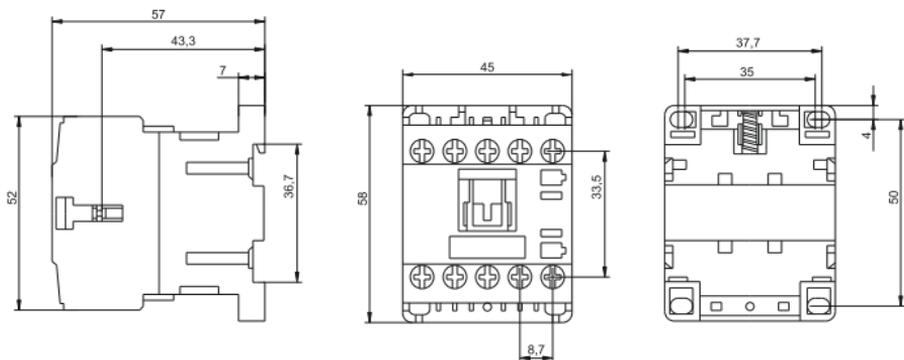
Габаритные и установочные размеры контакторов с катушкой управления на переменный ток / Figure 1 – Overall and mounting dimensions of contactors with the AC control coil
